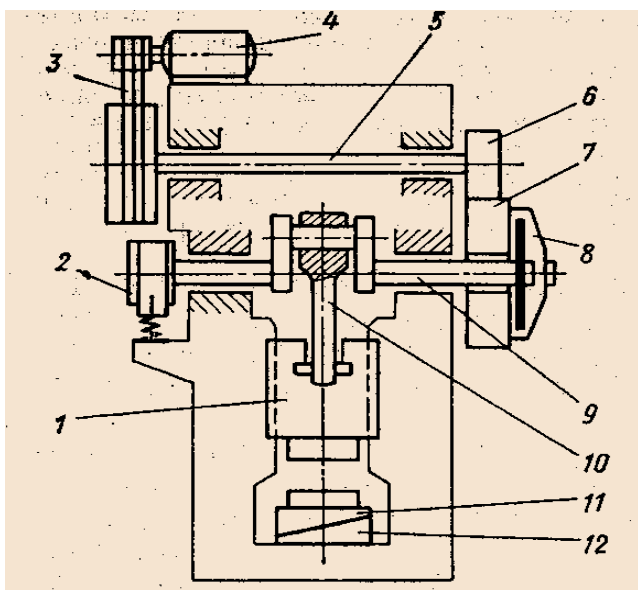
Кинематическая схема кривошипного горячештамповочного прессы (КГШП):
